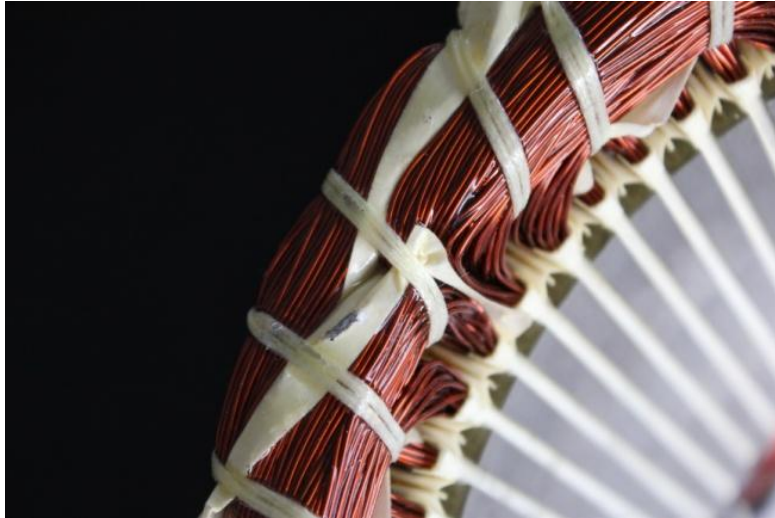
Detailansicht eines exemplarischen Wickelkopfs in E-Maschinen.
